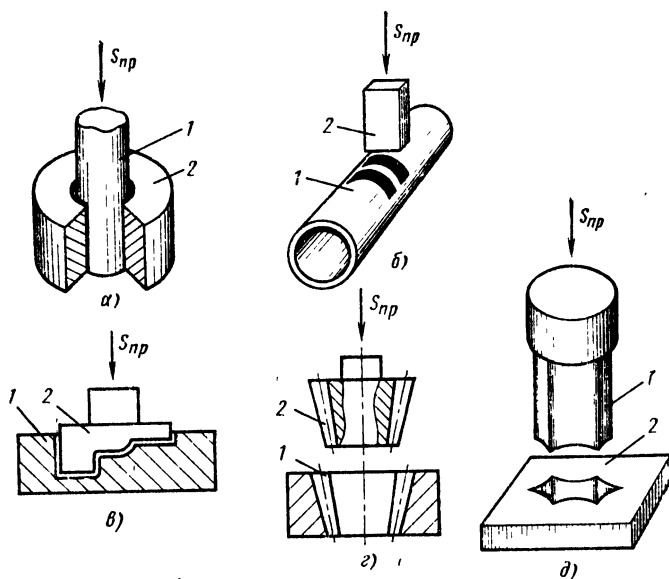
Схема формоутворення копіюванням геометричної форми електрода-інструмента
